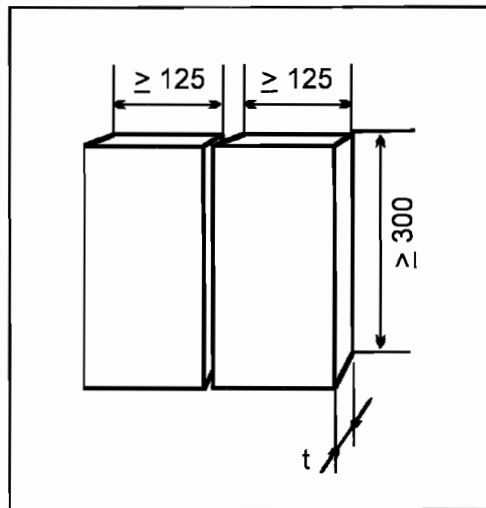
DIMENSIONES DEL CUPÓN DE PRUEBA PARA EL SOLDEO DE CHAPAS A TOPE (DIMENSIONES EN MILÍMETROS)
